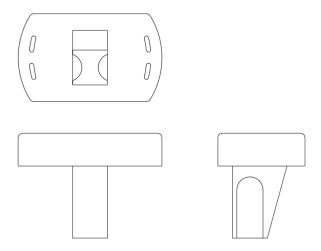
komponent piszczelowy po wykonaniu obróbki wstępnej
